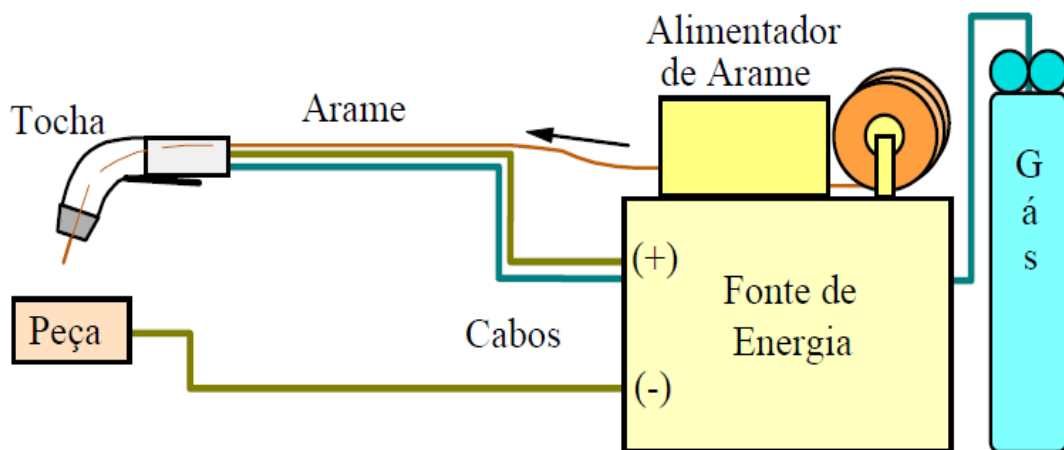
Desenho esquemático do equipamento de soldagem GMAW e FCAW, com proteção gasosa (MODENESI; MARQUES, 2006).
